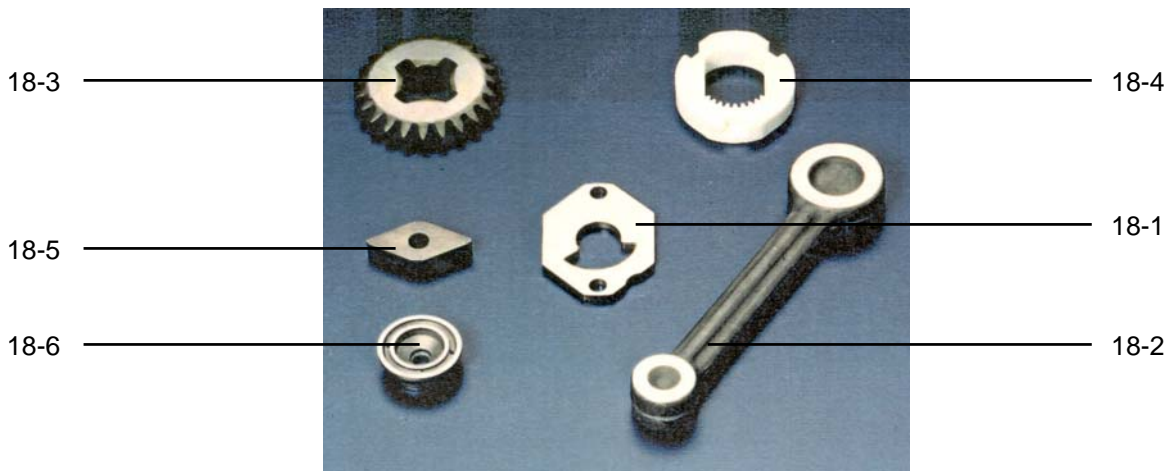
Beidseitig bearbeitete Flachhön-Werkstücke
